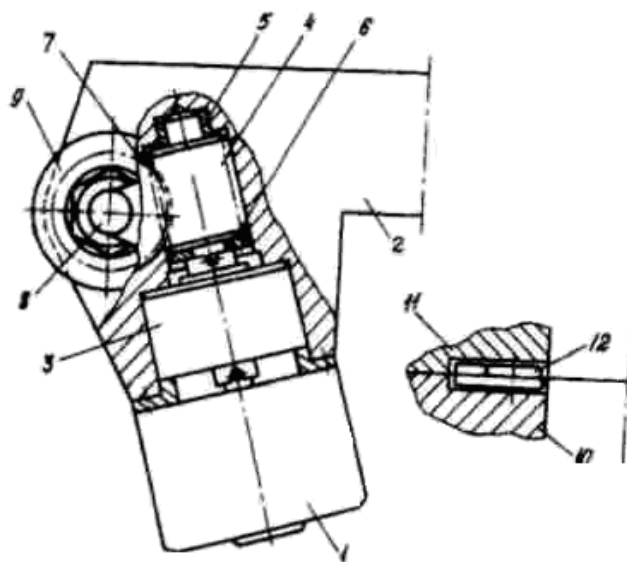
Эскиз резца с непрерывным обновлением режущей кромки и устройством выборки бокового зазора в червячной передаче
